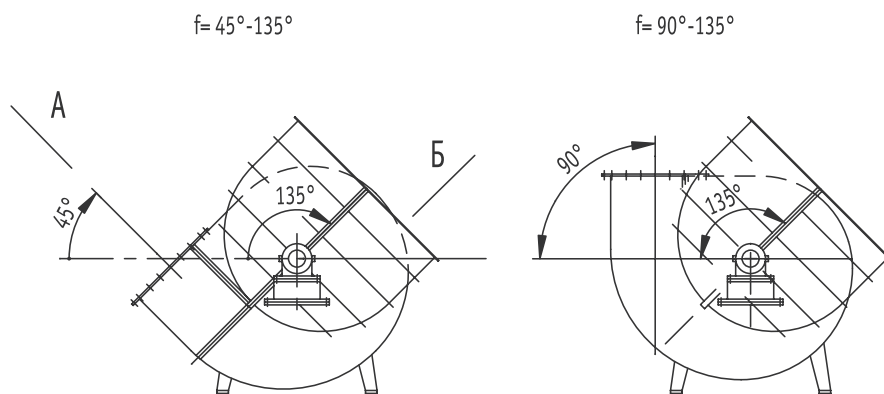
Положение корпуса тягодутьевых машин типа Д (ПР).
